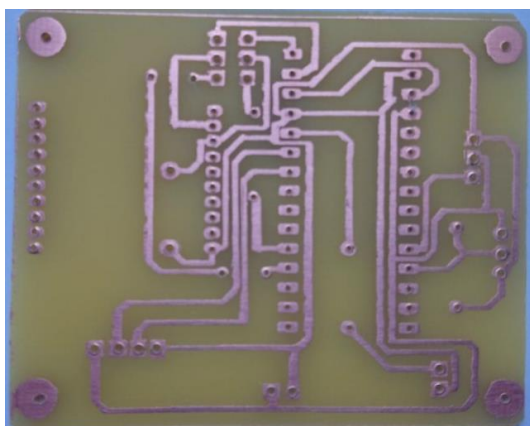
Placa electrónica Printed Circuit Board (PCB) para Nodo 2 y Nodo 3
